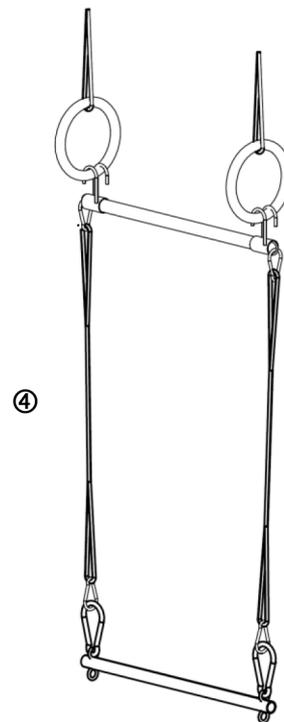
Zwei Trapezstangen Edelstahl mit Verbindungsseil
